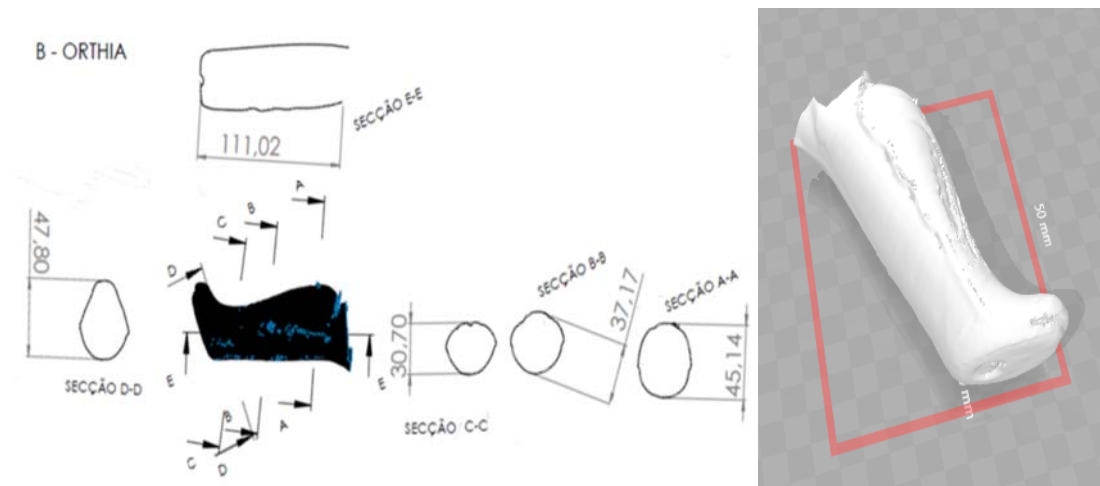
Dimensões Punho *Orthia* - dimensões em mm.
